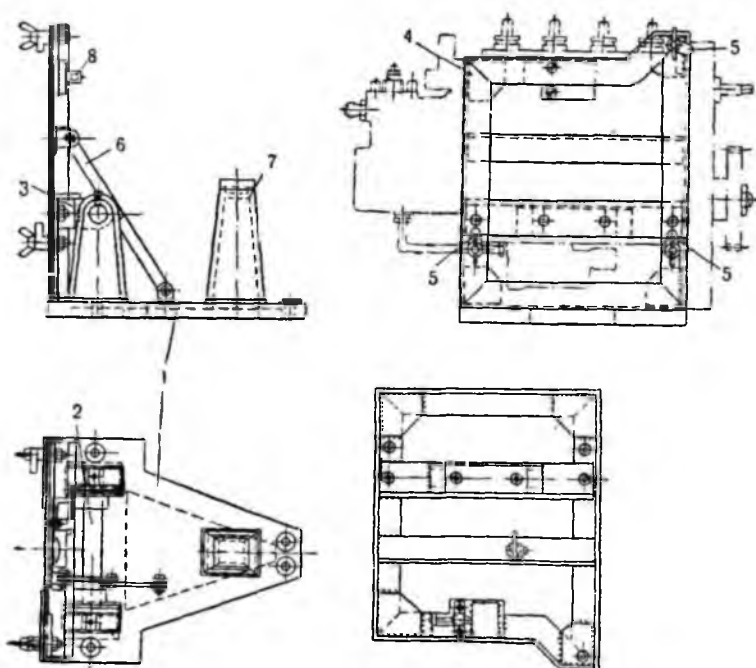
Стенд для разборки и сборки насосов ЧТЗ:
